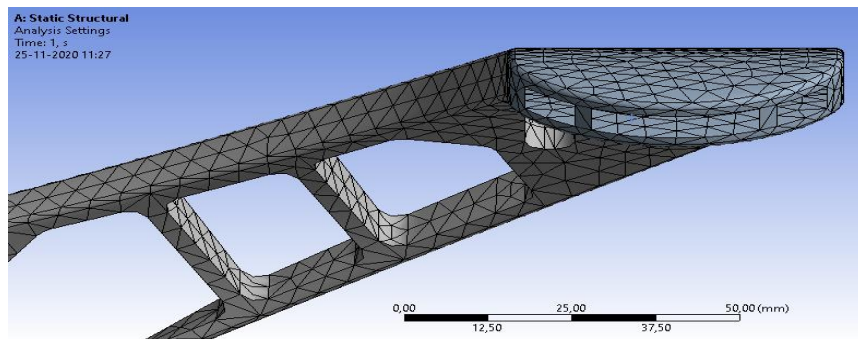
Vista 3 rediseño N°3 de eslabón pierna izquierda.
